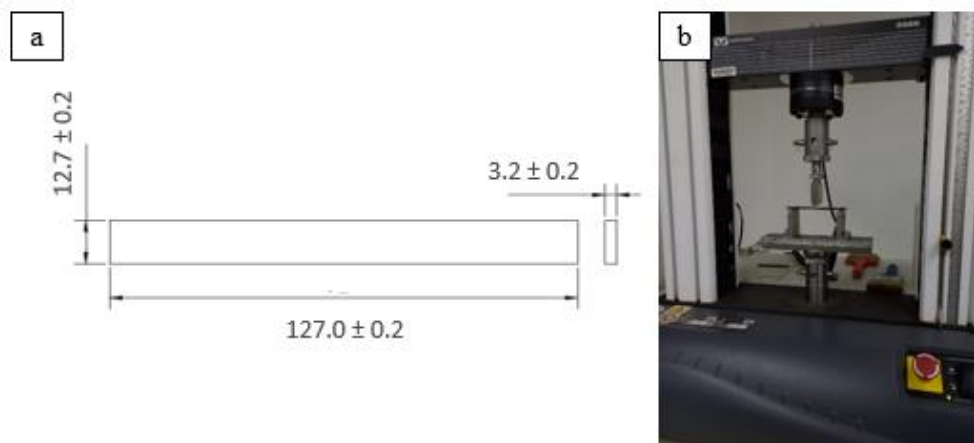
Ensayo a flexión. a) Dimensiones para probeta, las medidas están en mm, b) Ensayo
